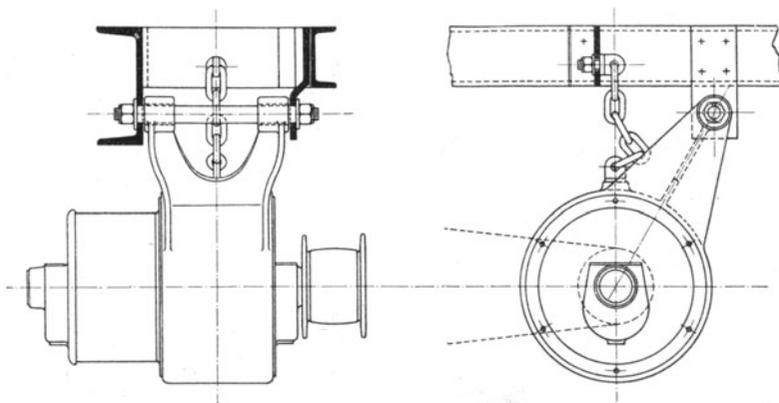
Maschinenaufhängung der Schweizer Bundesbahn für zwei- und dreiachsige Wagen.
